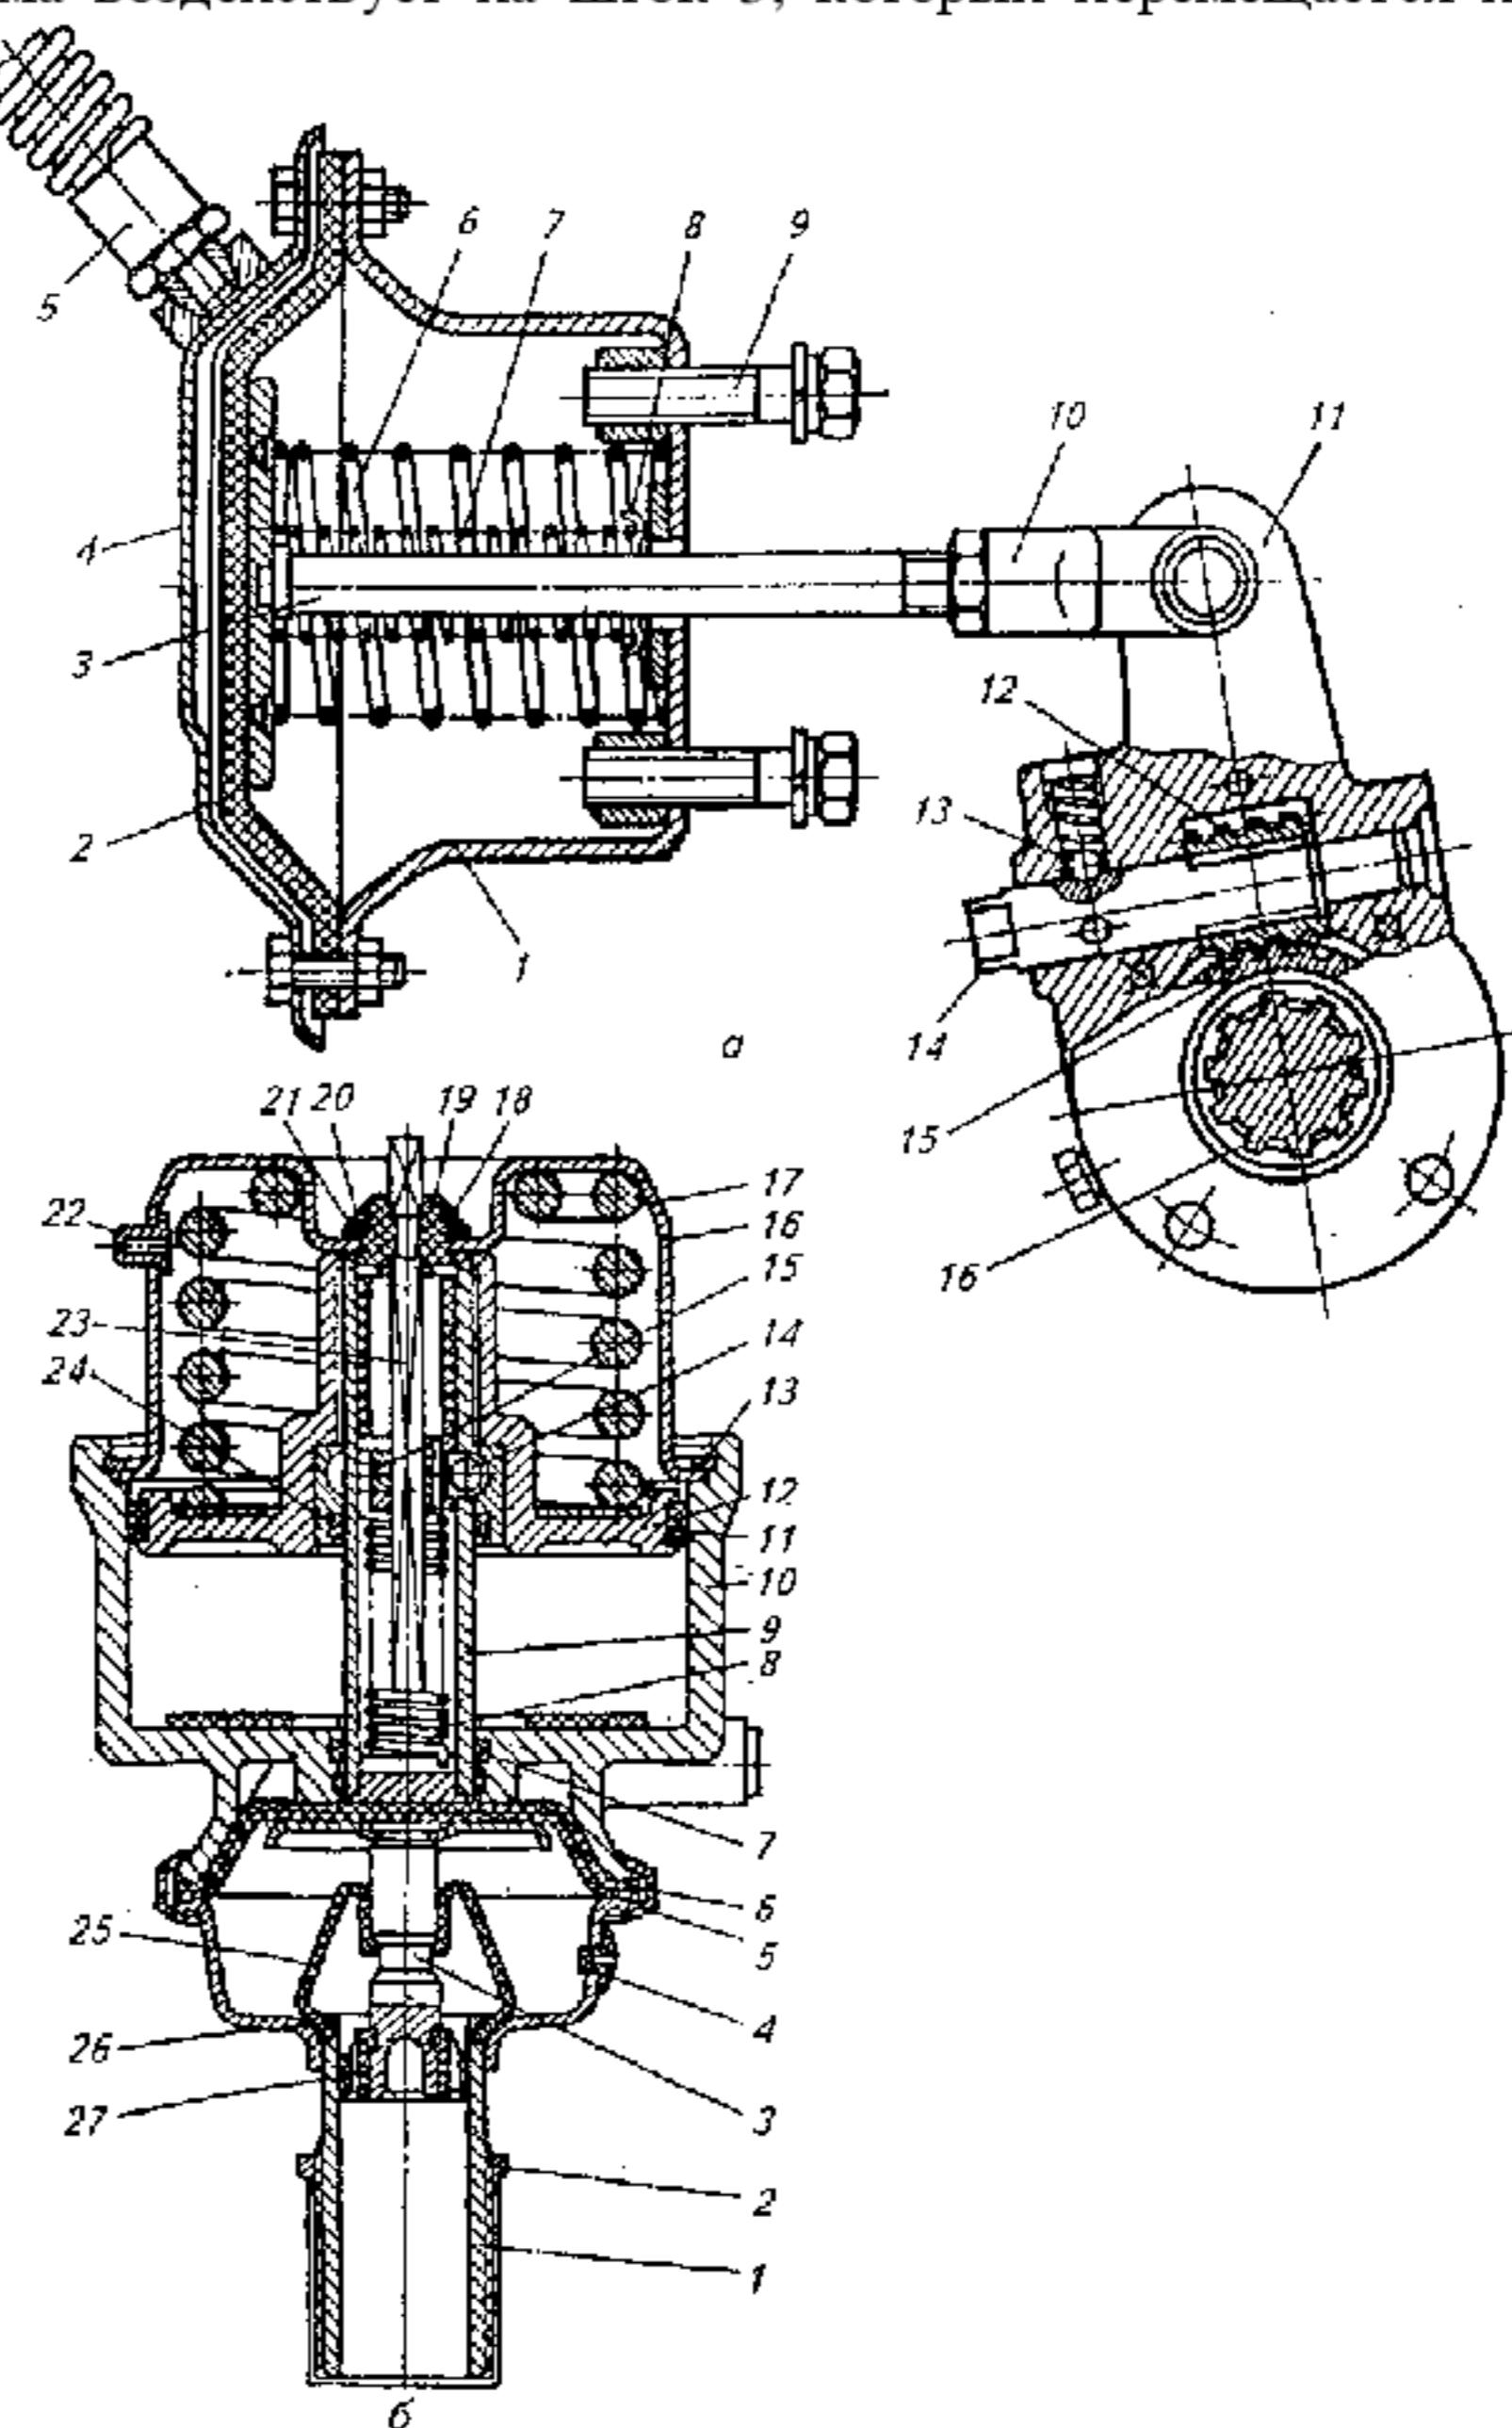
Тормозные камеры: а — мембранные: 1 — корпус камеры; 2 — диафрагма; 3
